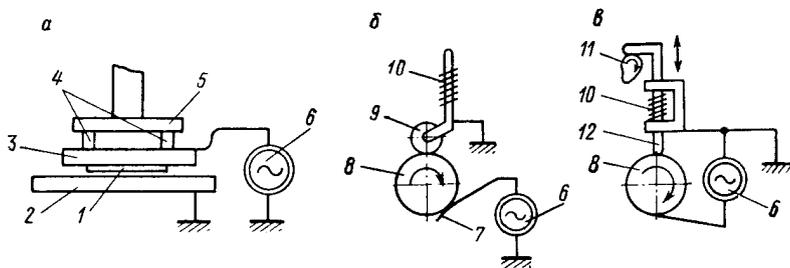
Схема высокочастотной сварки:
